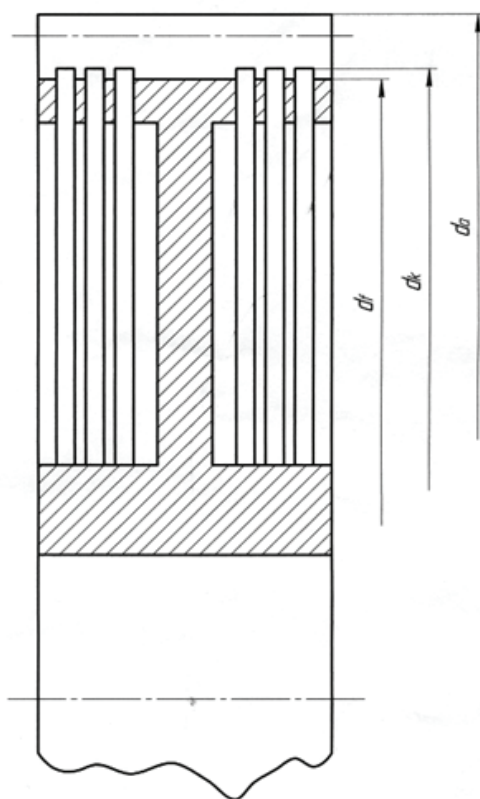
Колесо зубчатое с радиальными канавками диаметра d_k
